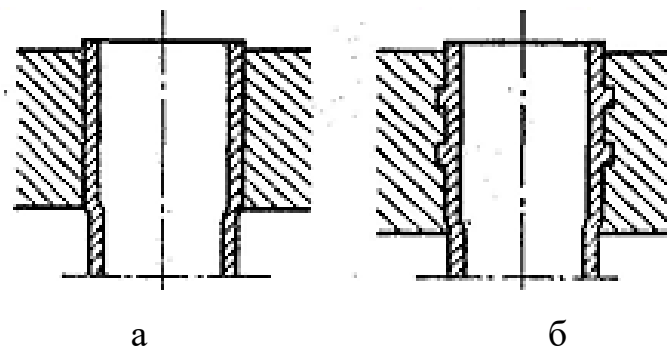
Розвальцьовування: а) гладке; б) з проточкою
